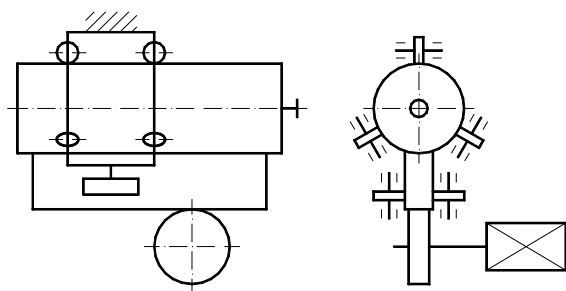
Základní vedení zde představuje pístnice motoru, pomocné vedení hranol
